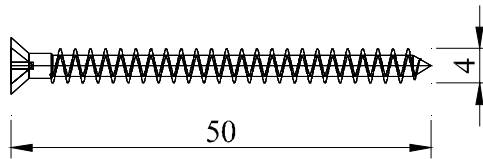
Deneylerde kullanılan kavela boyutları (ölçüler mm)
